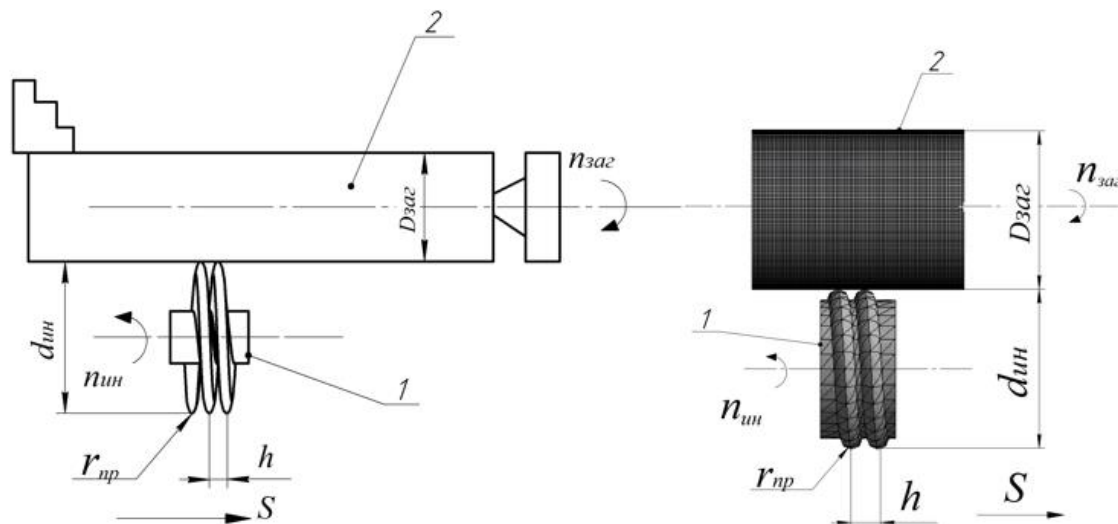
Кинематическая схема геликоидного ППД и конечно-элементная модель деформирования цилиндрической заготовки: 1 – рабочий инструмент; 2 – обрабатываемая заготовка;  $r_{пр}$  – профильный радиус;  $d_{ин}$  – диаметр инструмента;  $D_{заг}$  – диаметр заготовки;  $h$  – шаг витка инструмента
